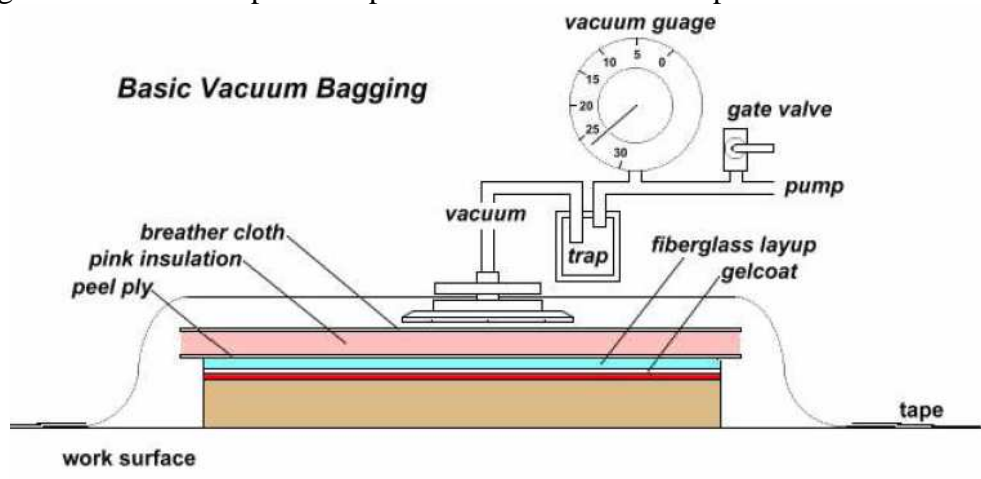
Técnica de fabricación mediante bolsa de vacío
